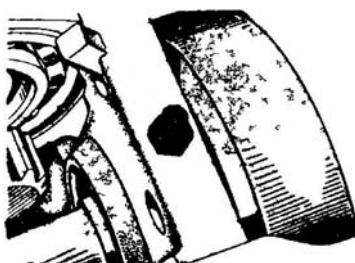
Выворачивание установочного винта подшипника вала коронной шестерни.
